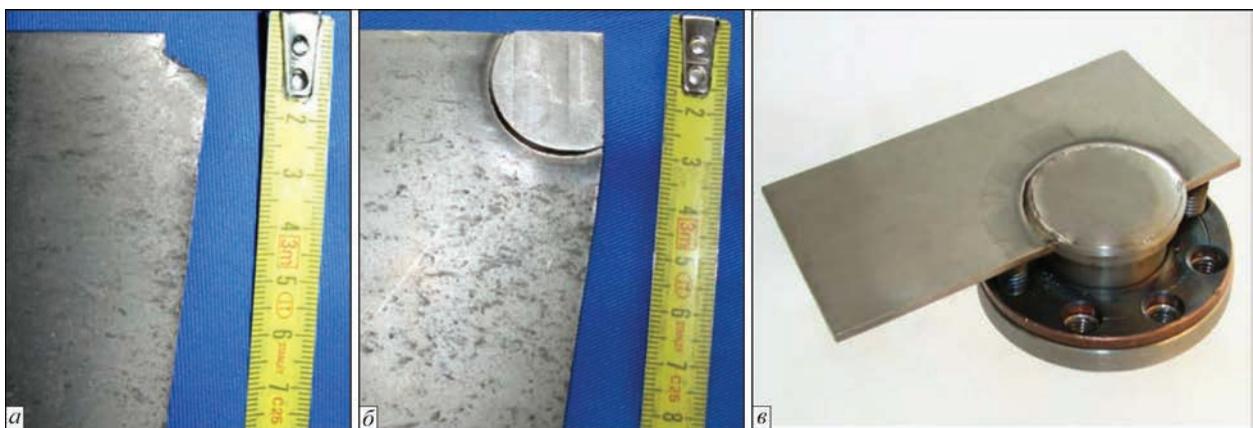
Ремонт точечных дефектов угла пера лопатки с применением цилиндрических ремонтных «вварышей»: а — поврежденный угол лопатки до ремонта; б — отремонтированный угол (края «вварыша» обрезаны после ЭЛС); в — сборочно-сварочная оснастка для ЭЛС цилиндрических «вварышей» (имитатор лопатки)
